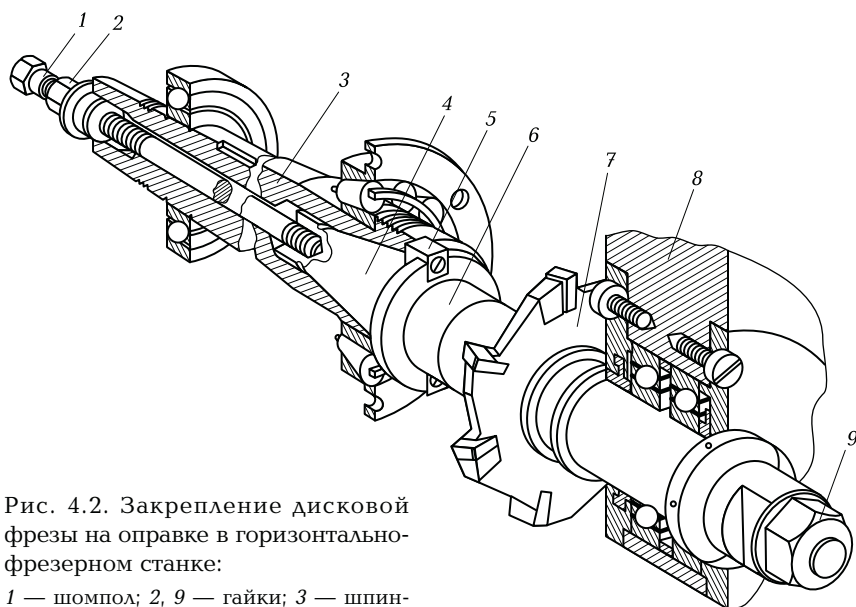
Закрепление дисковой фрезы на оправке в горизонтально-фрезерном станке:
